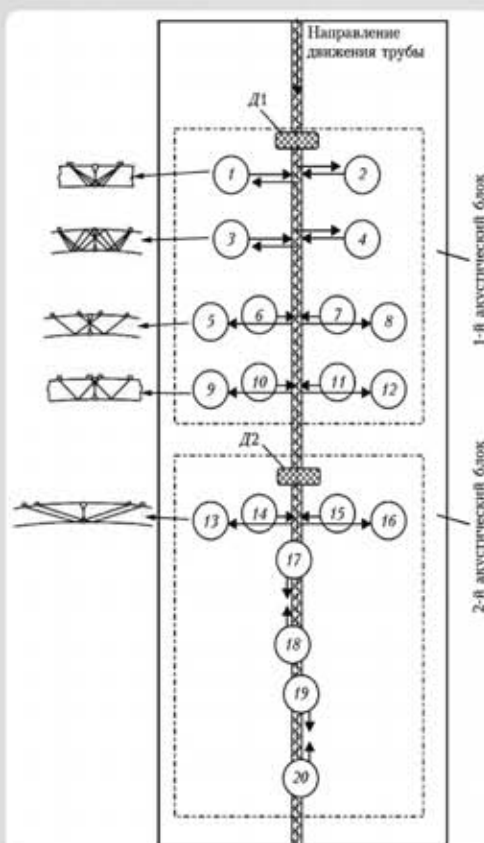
Схема расположения акустических головок при контроле продольных сварных соединений: D1, D2 — лазерные датчики слежения за валиком усиления сварного шва; 1 - 4 — группа наклонных ультразвуковых преобразователей для контроля на продольные дефекты; 5 - 16 — ультразвуковые преобразователи, работающие в схеме типа «тандем»; 9 - 16 — ультразвуковые преобразователи, стоящие на сварном шве и работающие в иммерсионном варианте на обнаружение поперечных дефектов
